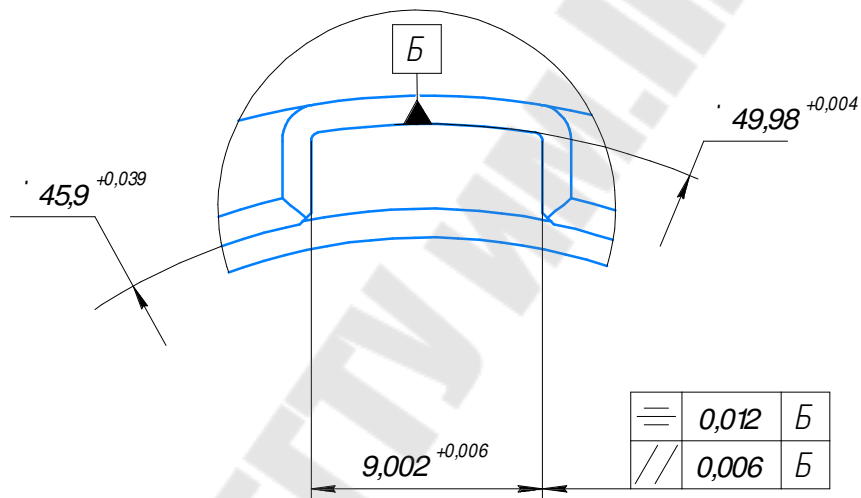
Эскиз калибра для контроля шлицевого вала.
